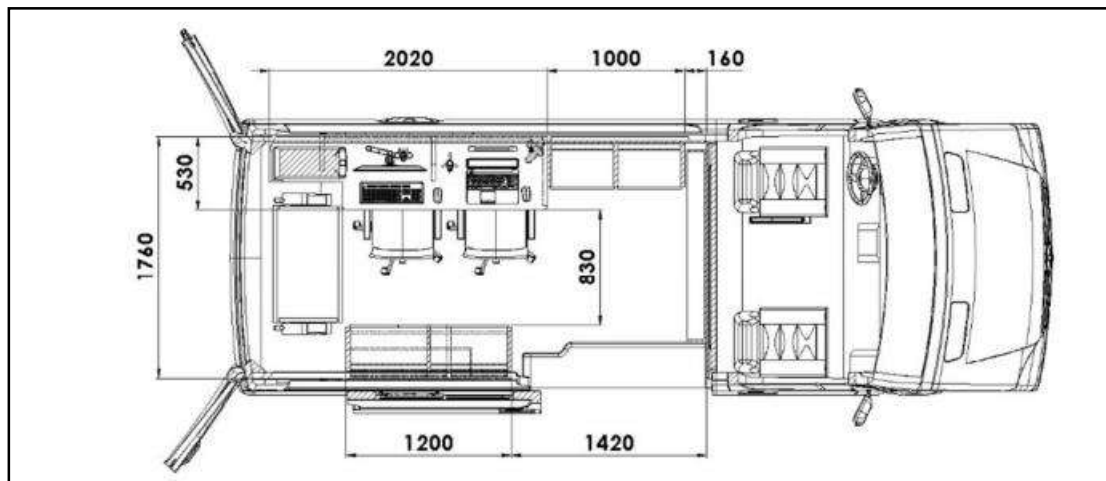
Planta esquemática da disposição dos equipamentos e mobiliários internos
